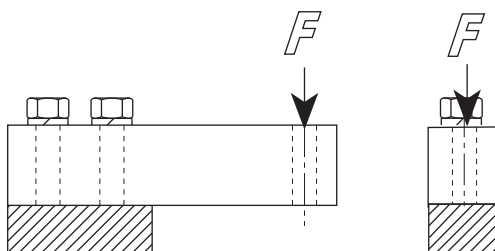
Celda de Carga Tipo Viga (Single-Ended Beam)
